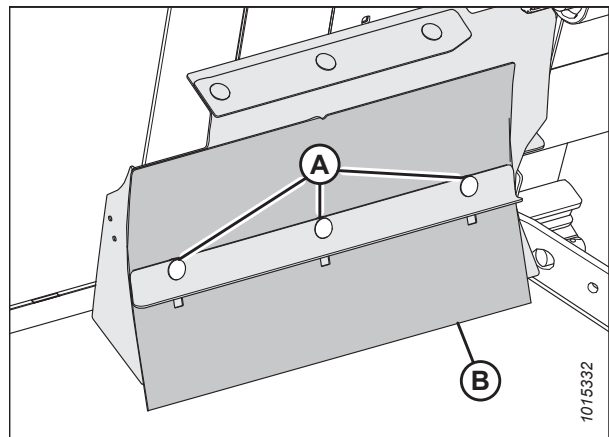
Vue avant du panneau de réglage en acier inoxydable
